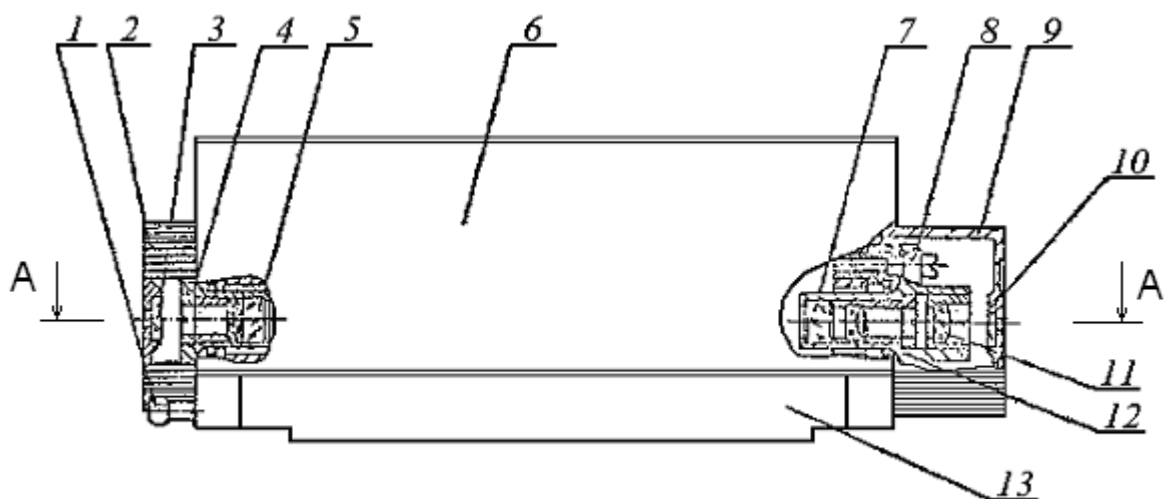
Излучатель лазера ЛТИ-407: 1 - штуцер; 2,9 – крышки узлов юстировки; 3,10 - светофильтры; 4,12 – оправы с оптикой; 5,7 – зеркала резонатора; 6 – корпус-крышка лазера; 8 - юстировочный винт; 11 - объектив телескопа; 13 – основание лазера; 14 – активный элемент; 15 - нелинейный элемент.
